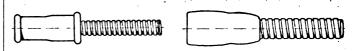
u. 49. Gummimuffen für Gasschläuche.
